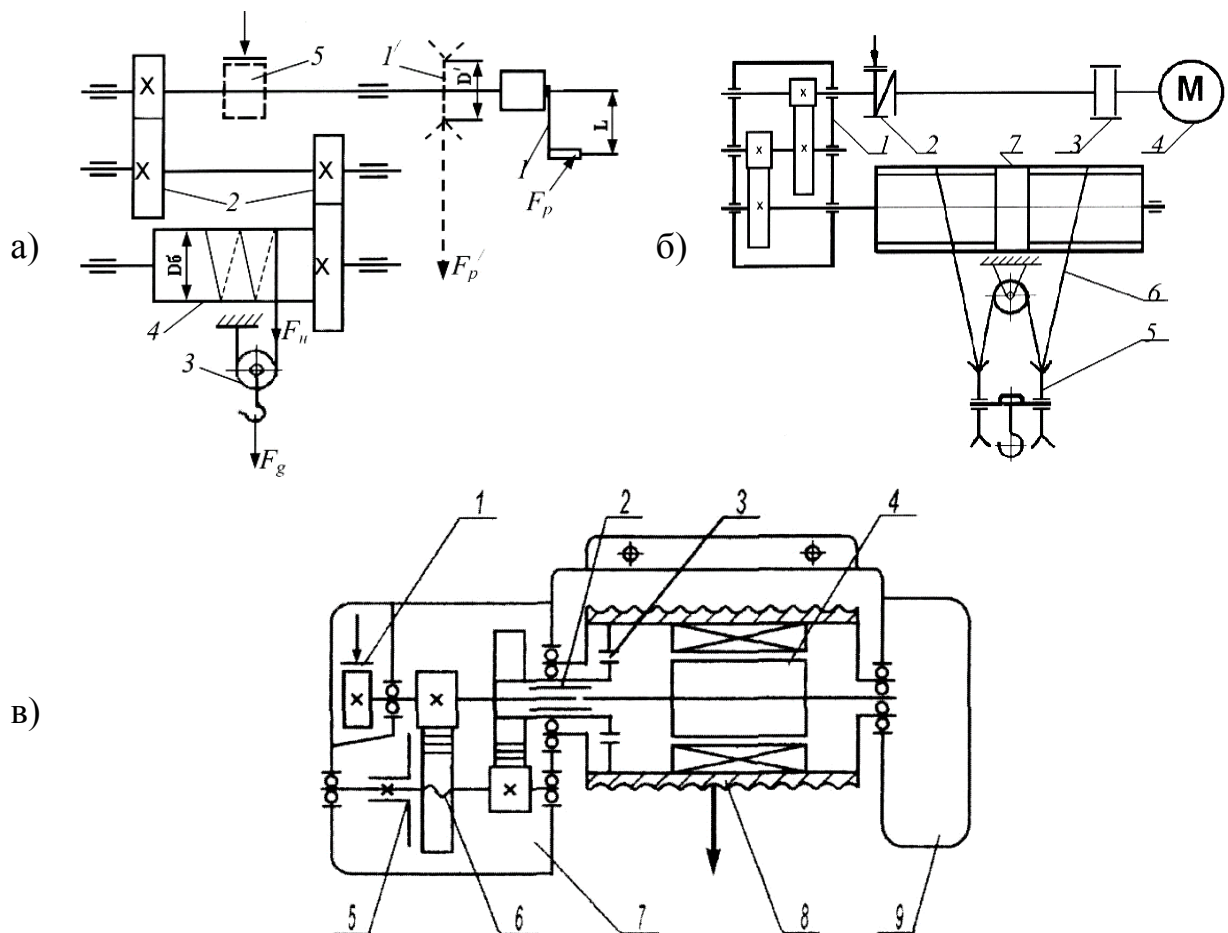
Механізми підйому: а – з ручним приводом (1 – ручка або привідна зірочка; 2 – відкриті зубчаті передачі; 3 – гакова підвіска; 4 – канатний барабан; 5 – гальмо); б – з електроприводом (1 – редуктор приводу; 2 – гальмо; 3 – муфта; 4 – електродвигун; 5 – гакова підвіска; 6 – канат); в – електроталі (1 – гальмо; 2 – жорстка муфта; 3 – зубчата муфта; 4 – електродвигун; 5 – маточина зубчатого колеса; 6 – зубчате колесо; 7 – редуктор приводу; 8 – барабан; 9 – корпус)
